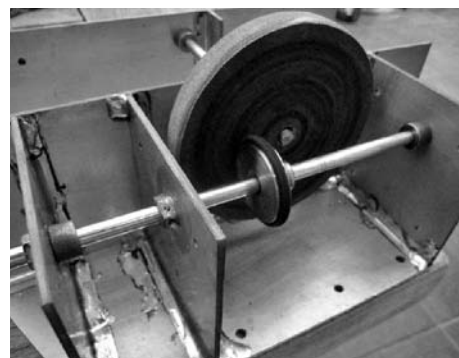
Het werkingsprincipe van de wikkelmachine.
